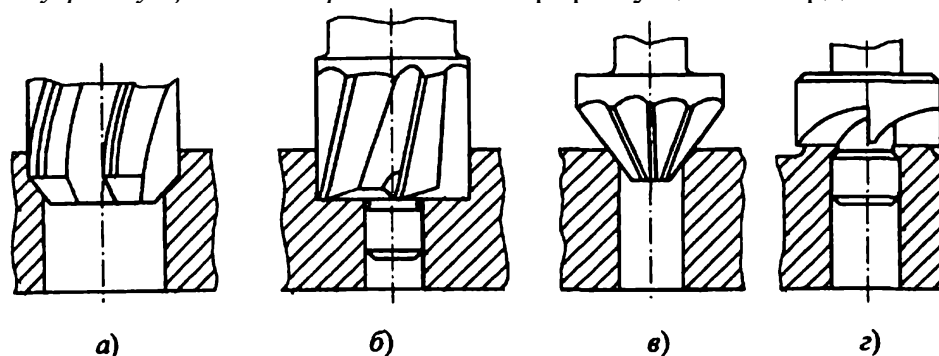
Типы зенкеров: а – цилиндрический зенкер; б, в и з – зенковки
